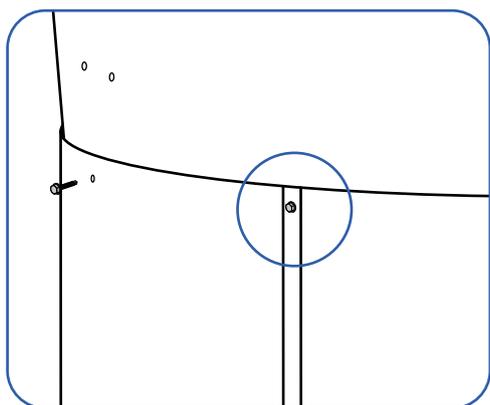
a. Colocar primero el tornillo que une las dos partes de la extensión.
